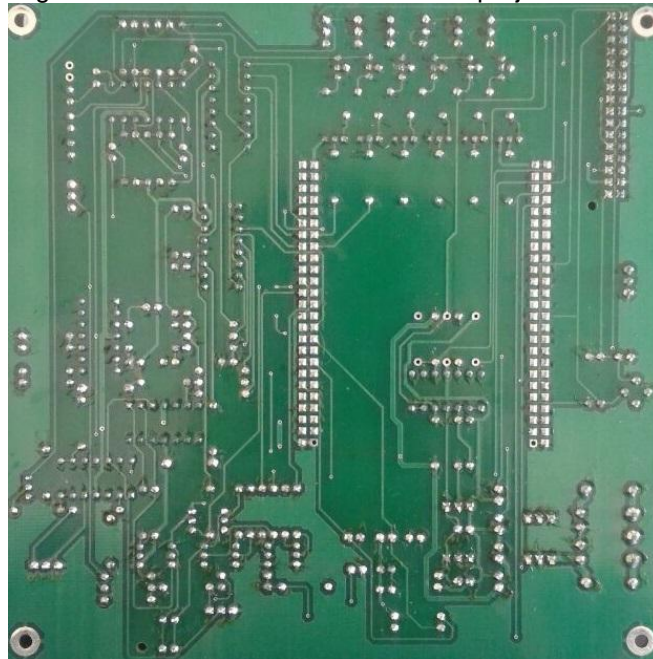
Componentes soldados na PCI do projeto final
